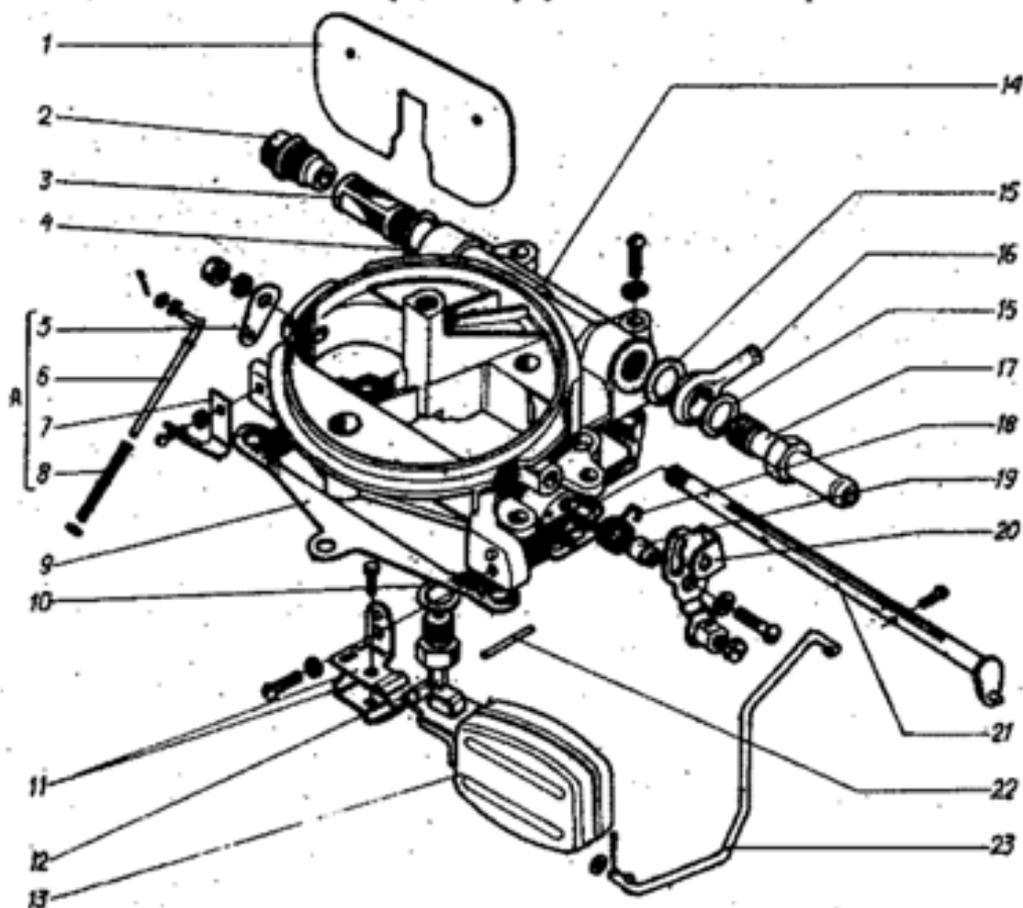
Детали крышки поплавковой камеры: 1 - воздушная заслонка; 2 - пробка фильтра; 3 - сетка фильтра в сборе; 4 - прокладка пробки фильтра; 5 - рычаг; 6 - штанга; 7 - кронштейн; 8 - компенсационная пружина; 9 - прокладка поплавковой камеры; 10 - прокладка клапана подачи топлива; 11 - кронштейн тяги воздушной заслонки; 12 - клапан подачи топлива; 13 - поплавок; 14 - крышка поплавковой камеры; 15 - прокладка; 16 - патрубок слива топлива; 17 - патрубок подачи топлива; 18 - пружина оси привода воздушной заслонки; 19 - втулка оси привода воздушной заслонки; 20 - рычаг привода воздушной заслонки; 21 - ось воздушной заслонки; 22 - ось поплавка; 23 - тяга малых оборотов.
